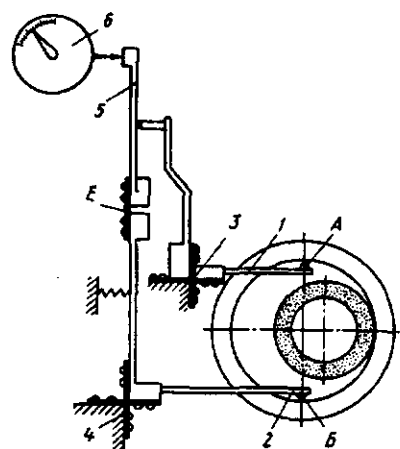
Схема индикаторного рычажного прибора для визуального измерения при внутреннем шлифовании
